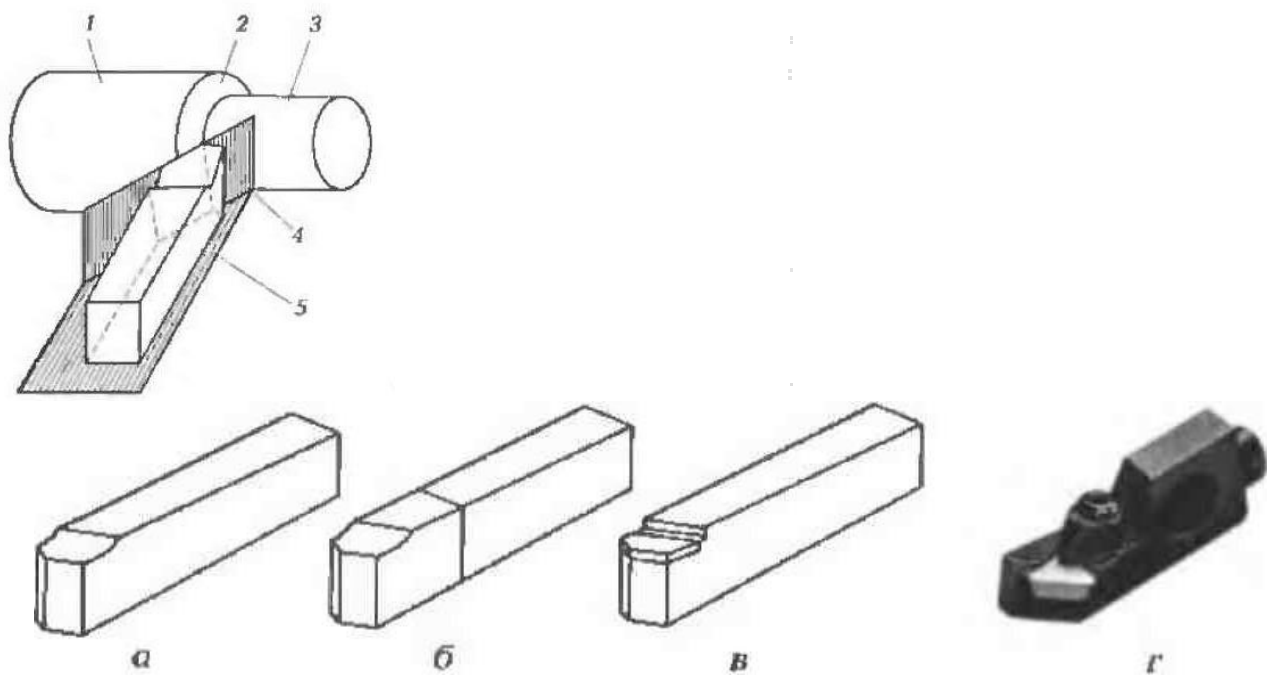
Типы резцов, определяемые по способу крепления их режущей части:
